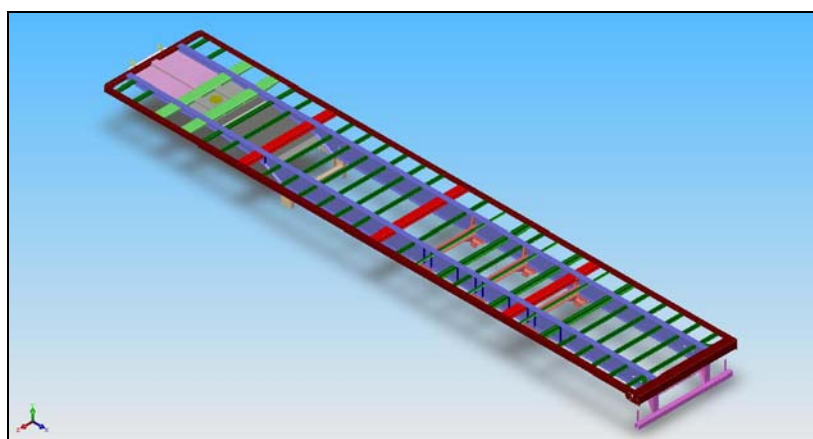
Modelo 3D do chassis construído em SolidWorks
